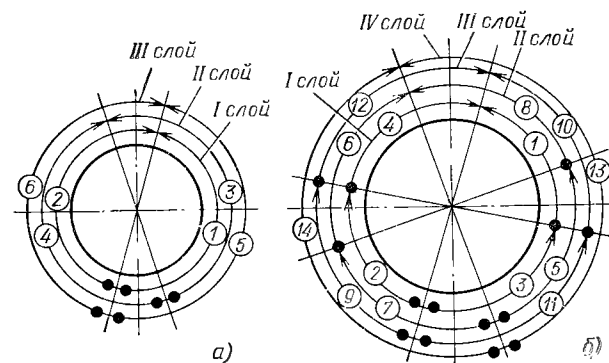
Порядок наложения слоев при сварке вертикального неповоротного стыка труб одним сварщиком.
